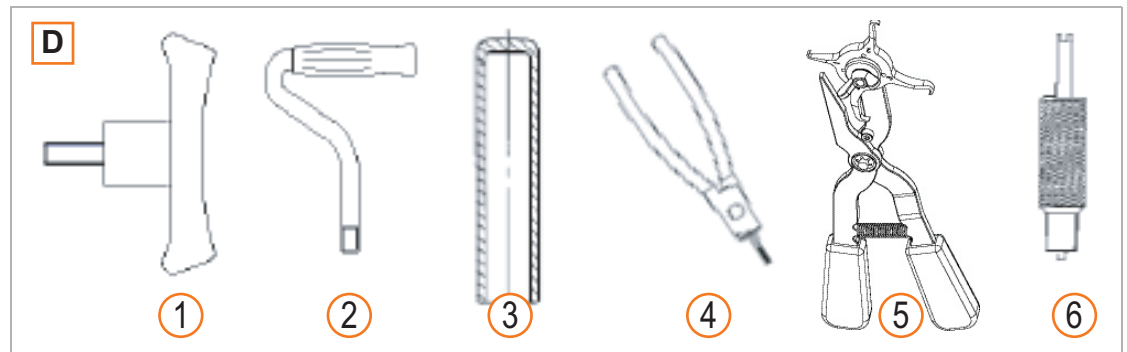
Werkzeugsatz 2480.00.50.11
